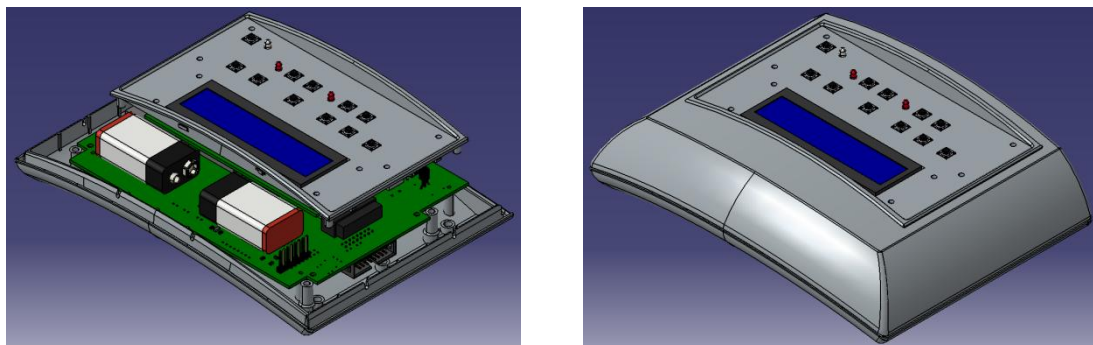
Ensamblaje final del gabinete. A la izquierda, vista sin la tapa frontal del gabinete, para apreciar las partes. A la derecha, gabinete completo y cerrado.
